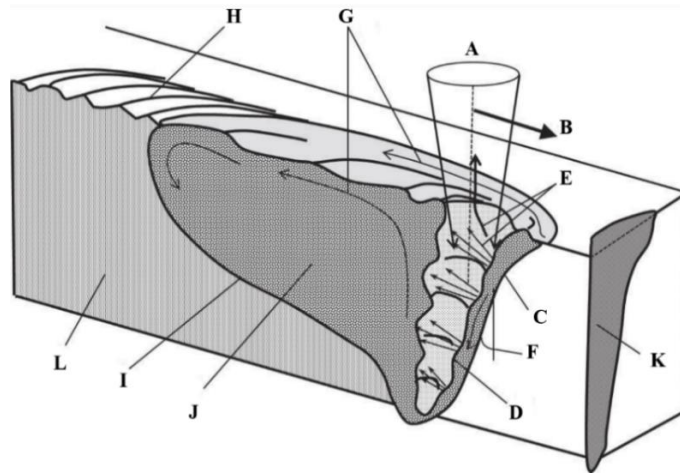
Dessin général d'un cordon de soudure, par Fabbro [46] . A : faisceau laser; B : Direction du lasage; C : front avant du keyhole; D : bosses du front avant; E : jet de vapeur; F : inclinaison du front avant; G : déplacements convectifs du bain; H : Structure en chevrons; I : Front de solidification; J : Bain de fusion; K : projection du 1/2 profil du keyhole ; L : matériau resolidifié
